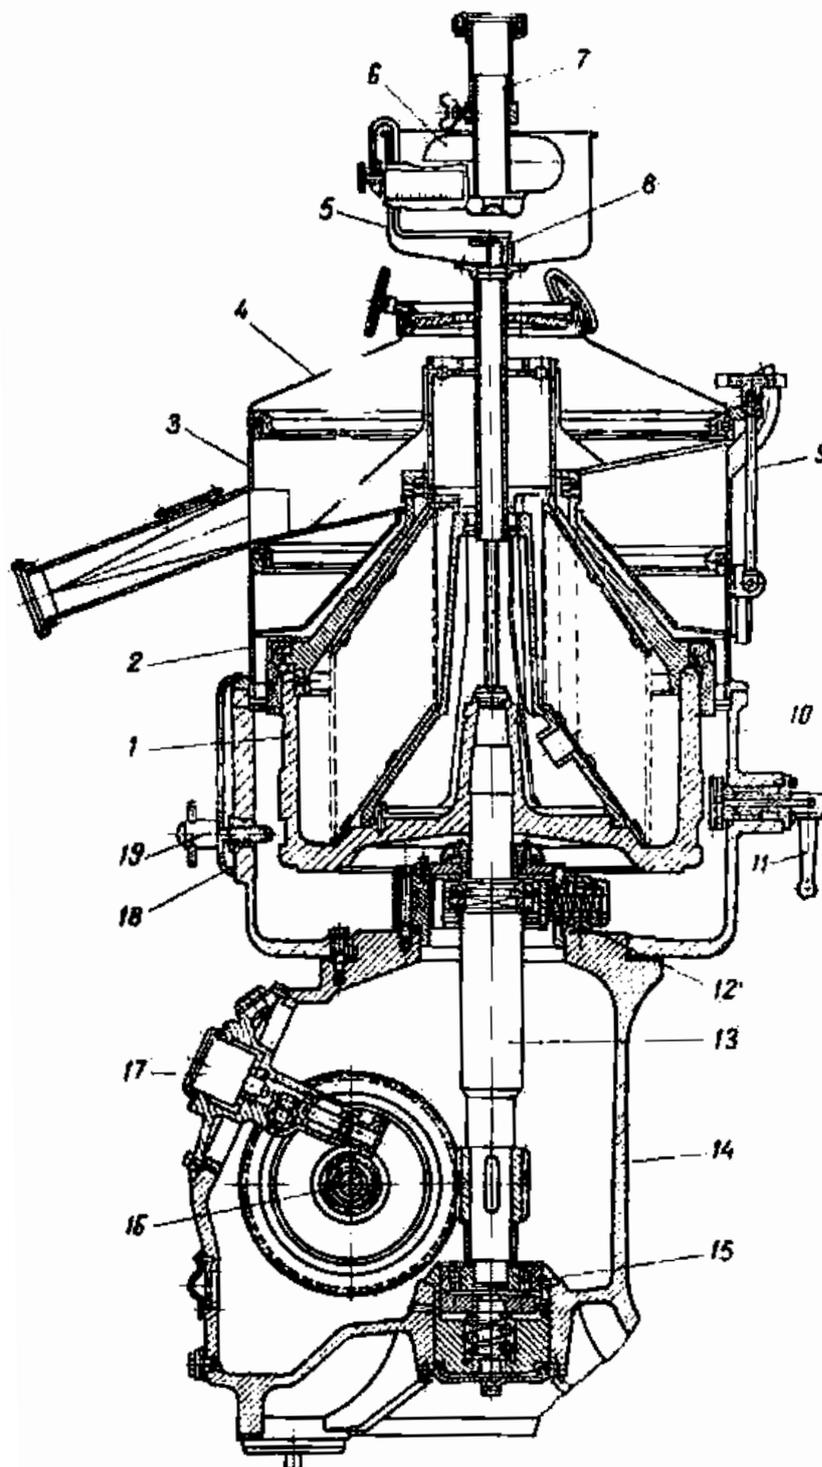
Сепаратор ОСМ-5 для высокожирных сливок: 1 - барабан; 2 - приемник «пахты»; 3 - приемник высокожирных сливок; 4 - крышка; 5 - поплачковая камера; 6 - поплавок; 7 - питающая труба; 8 - кран; 9 - зажим; 10 - чаша станины; 11 - тормоз; 12 - горловая опора; 13 - веретено; 14 - станина; 15 - нижний подшипник; 16 - горизонтальный вал; 17 - тахометр; 18 - скоба прижимная; 19 - винт упора
